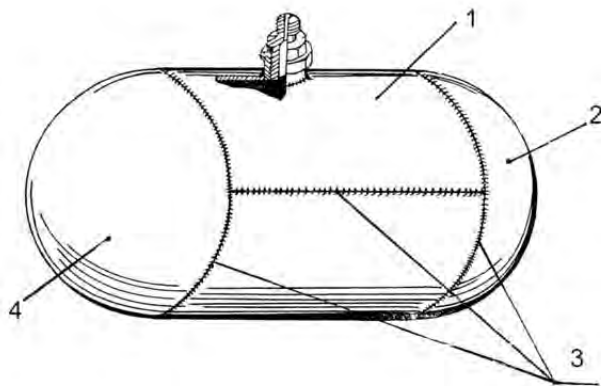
Типовая конструкция сварных сосудов из алюминиевых сплавов:
